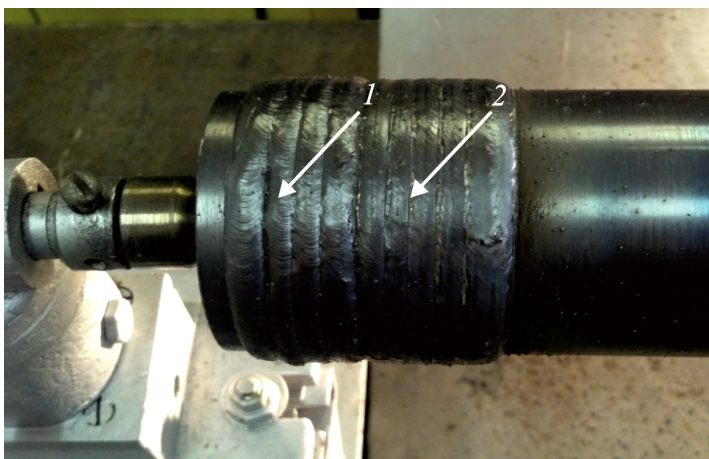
Наплавленный металл: 1 – шов, выполненный без горелки с неплавящимся электродом; 2 – шов, выполненный с горелкой с неплавящимся электродом
